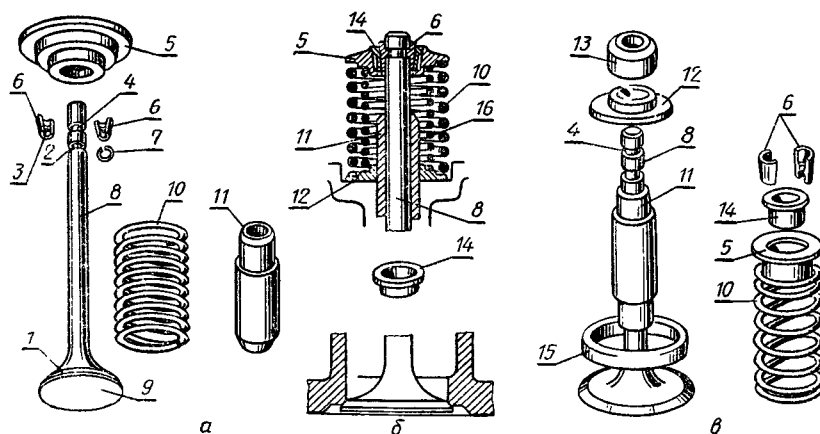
Клапан, пружина и детали ее крепления механизма газораспределения:
